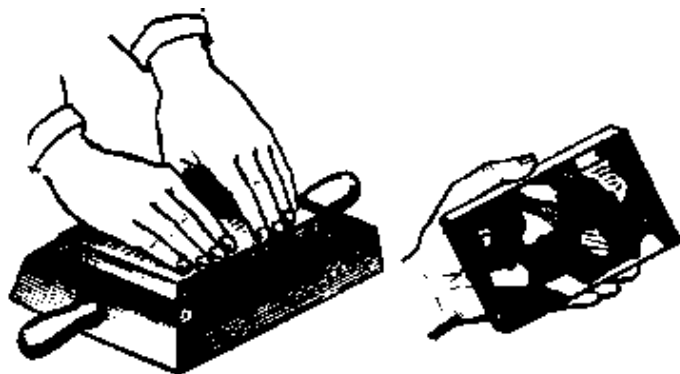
Визначення на оброблюваній поверхні місць шабрування
